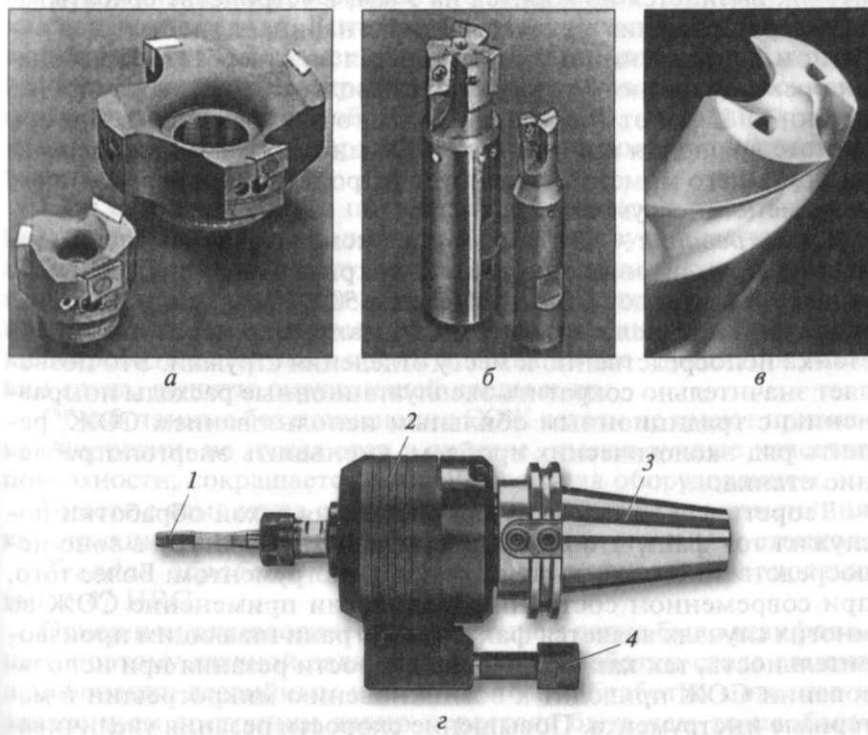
Инструменты, применяемые при высокоскоростном резании: *а, б* — соответственно сбалансированные торцевые и концевые фрезы со сменными пластинами; *в* — цельное твердосплавное сверло с винтовыми канавками для подвода СОЖ; *г* — резьбонарезное устройство; 1 — метчик; 2 — патрон; 3 — хвостовик оправки; 4 — рычаг
